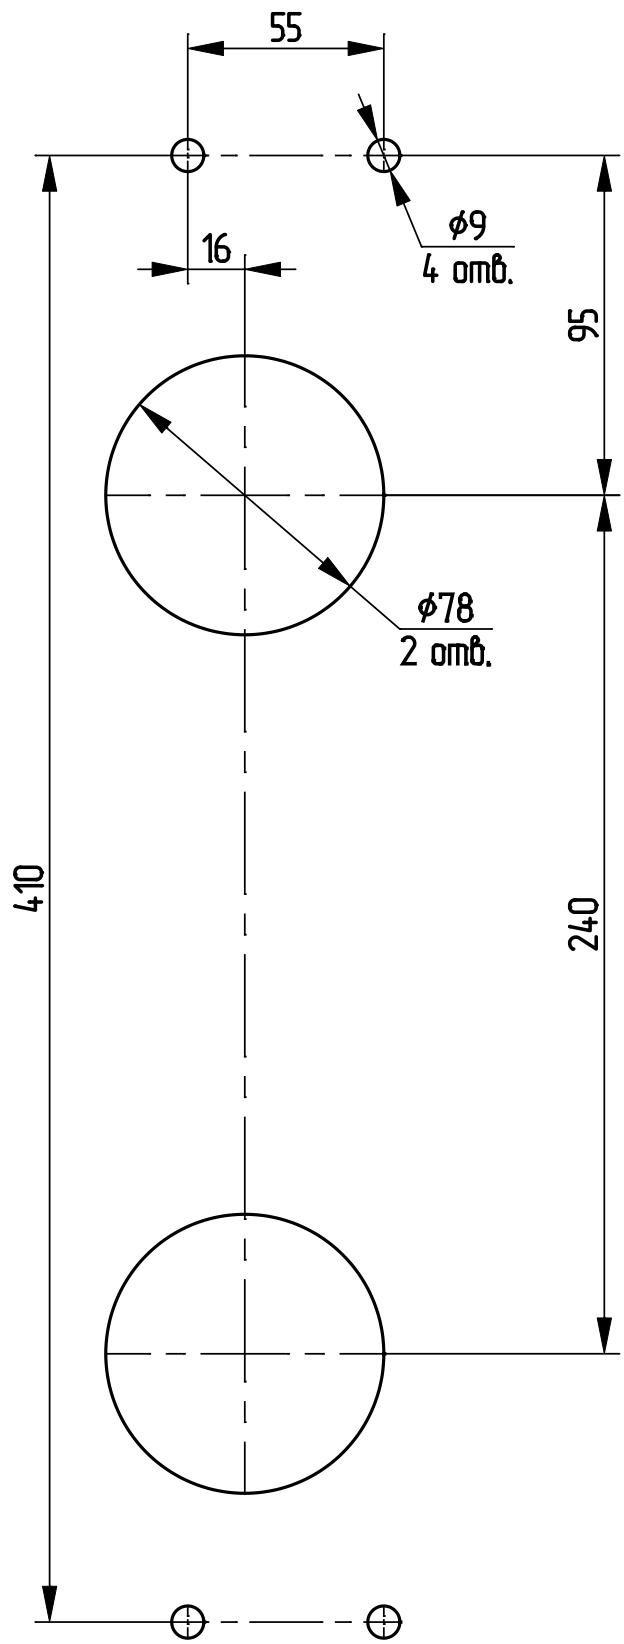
Разметка отверстий для установки приводов ПРК-10Б-24 (вид спереди)
